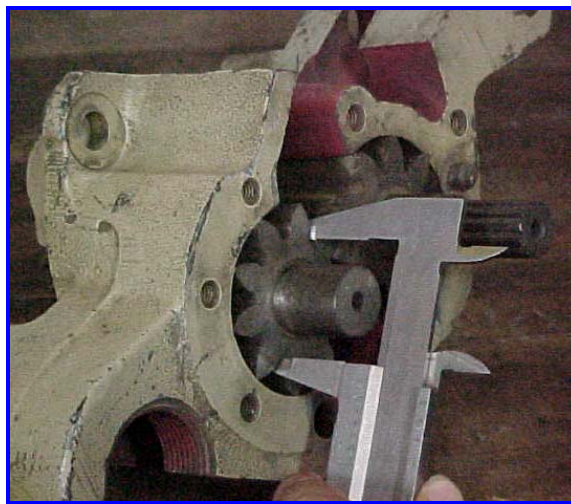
Medición del diámetro interno engranajes bomba de aceite.
